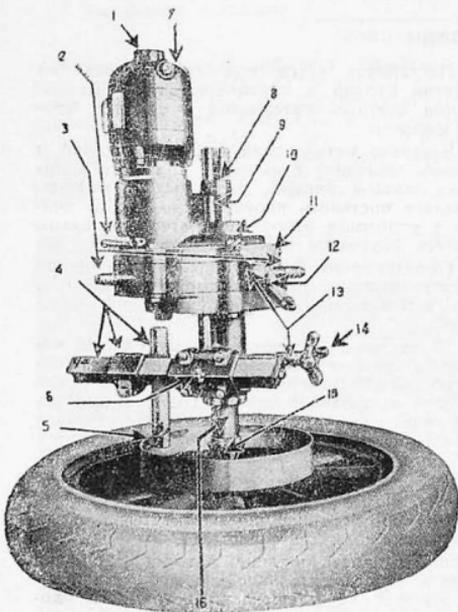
Переносное приспособление для расточки и обточки тормозных барабанов
